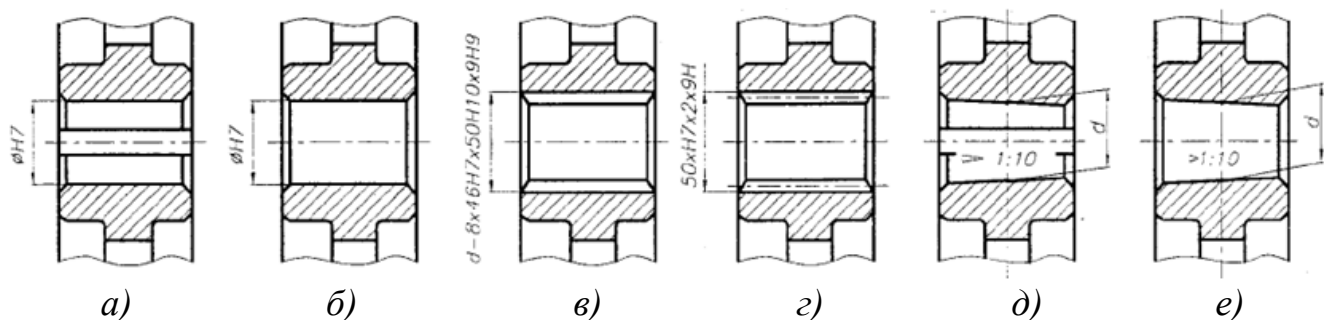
Отклонения формы, расположения поверхностей ступиц шкивов плоскоремённых передач и их шероховатости
